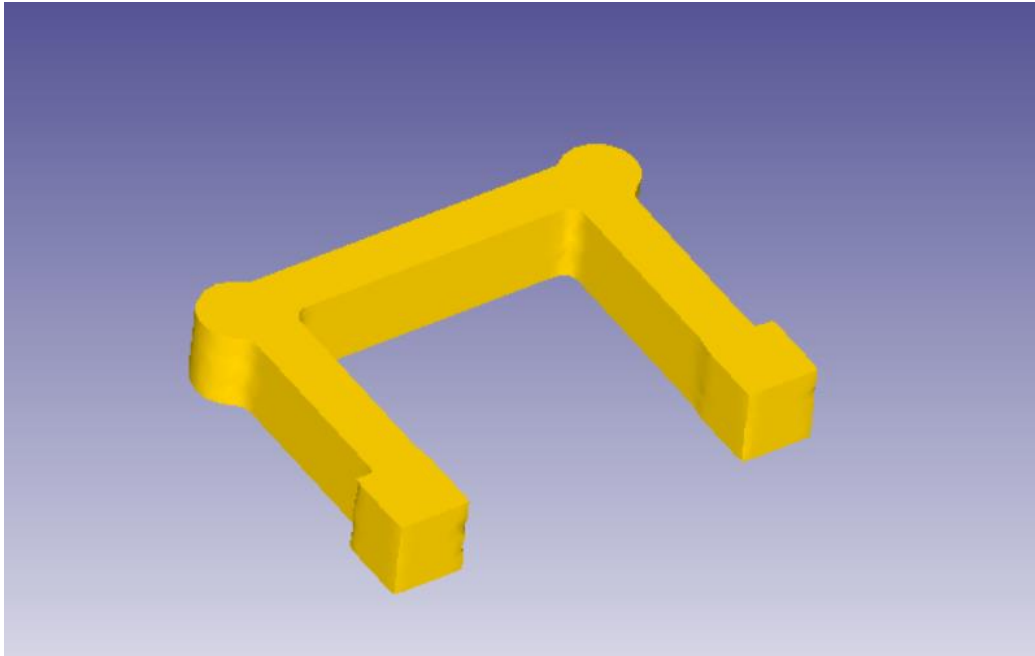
Нова заготовка отримана з товстолистого прокату
